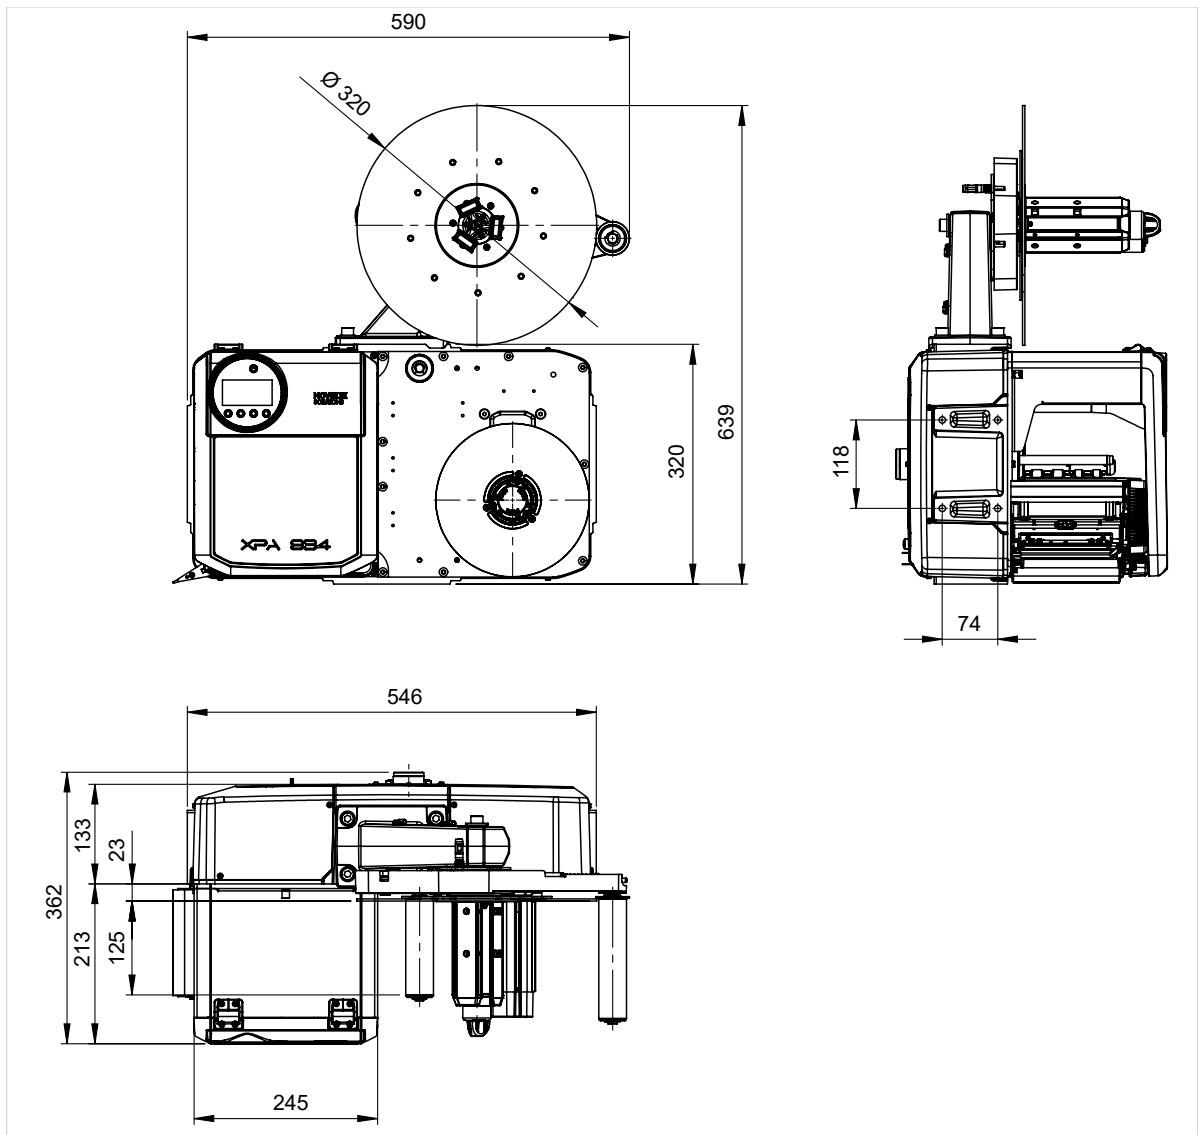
Dimensiones del XPA 934 LH con desenrollador Pro 300.
